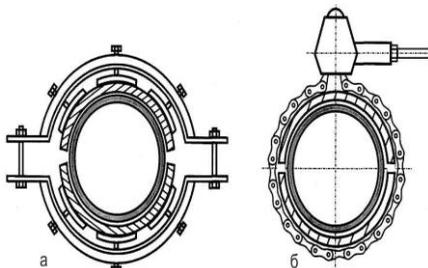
Приспособления для сборки полуцилиндров муфты:
